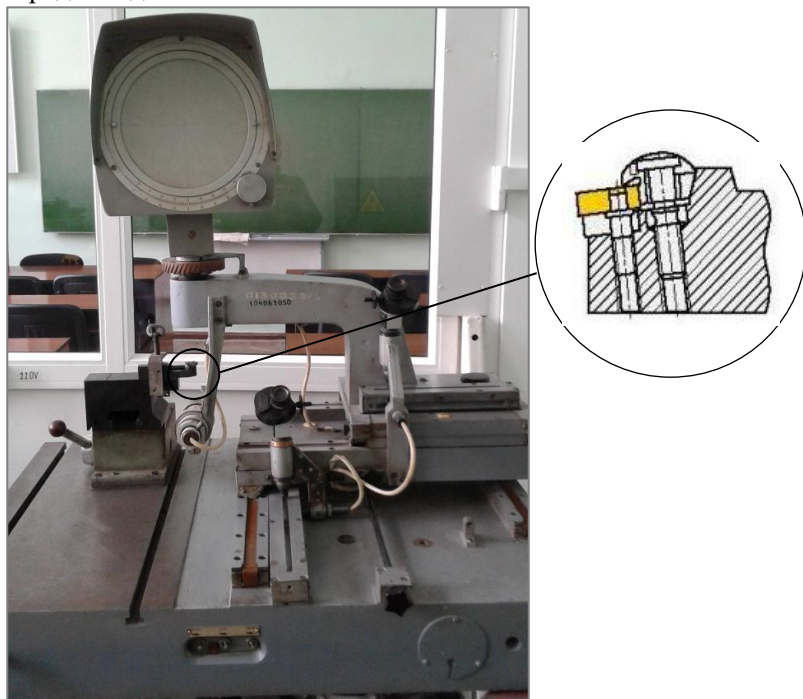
Вимірювальний пристрій та схема базування пластинки.
